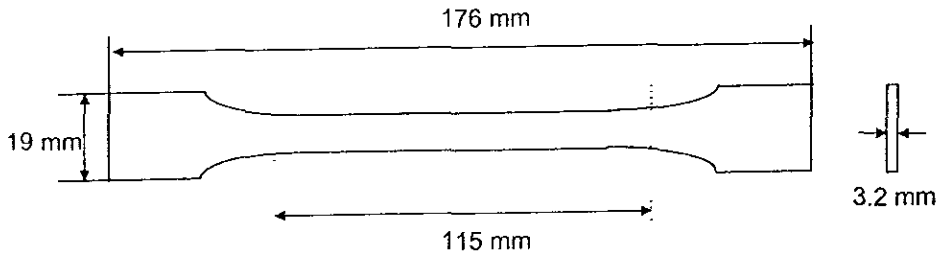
Dimensiones del espécimen para la prueba de tensión
